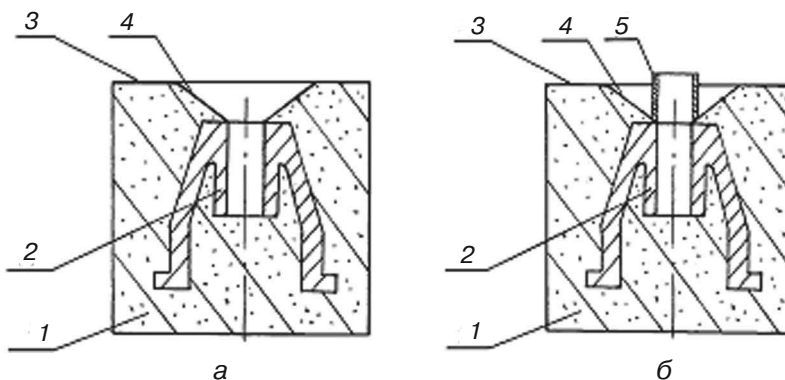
Литейная форма: в разрезе по оси цилиндра отливки (а); то же с патрубком, установленном на отливке (б): 1 – песок; 2 – цилиндр (гильза) отливки блока цилиндров; 3 – контрлад; 4 – естественный откос песка; 5 – патрубок
